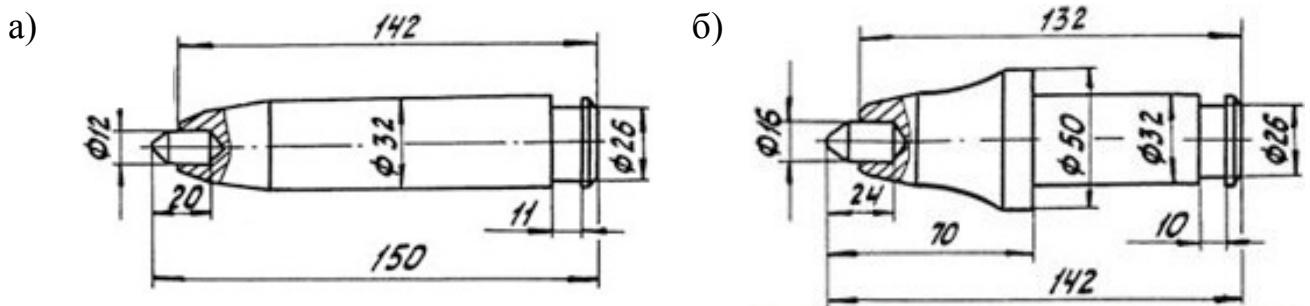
Конструкции резцов: а) – резец РКС-2; б) – резец ПС2-16
